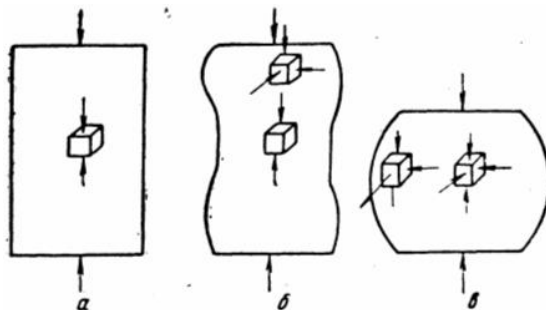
Схемы напряжений при осадке цилиндрических заготовок:
